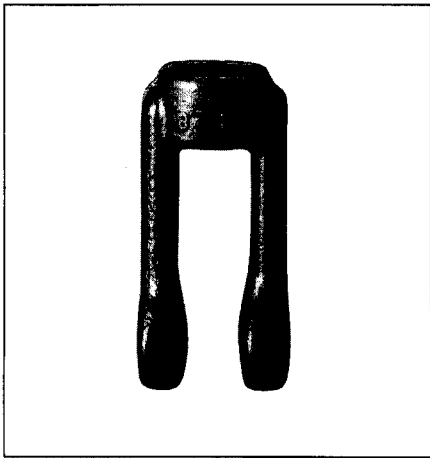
Gewindeöse (0,15 kg) für die Aufhängung von Rohrleitungen aus C 22.8
